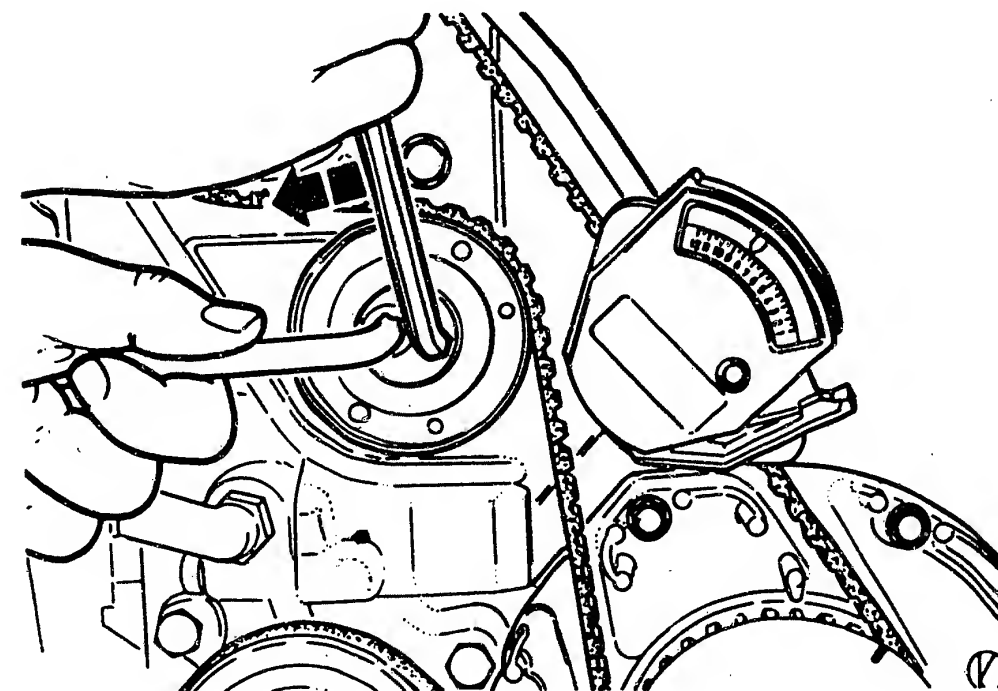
Diesel-Motor: Spannen des Zahnriemens mit der exzentrischen Spannrolle.
